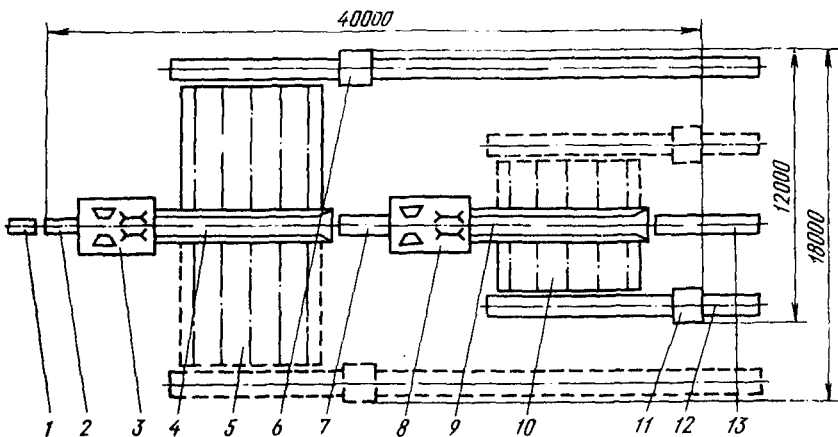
Схема фрезерно-пильных линий ЛФП-2 и ЛФП-3:
